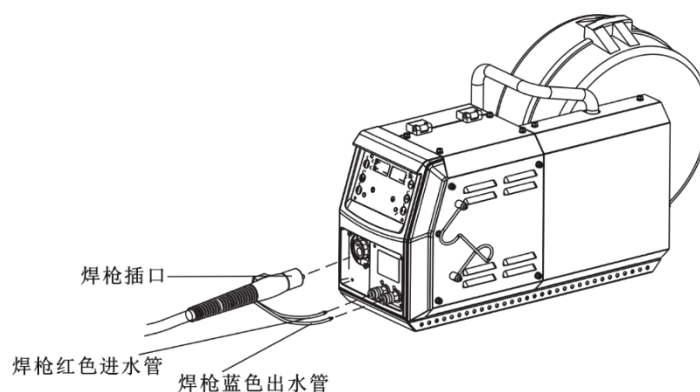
封闭式手工送丝机焊枪连接示意图
